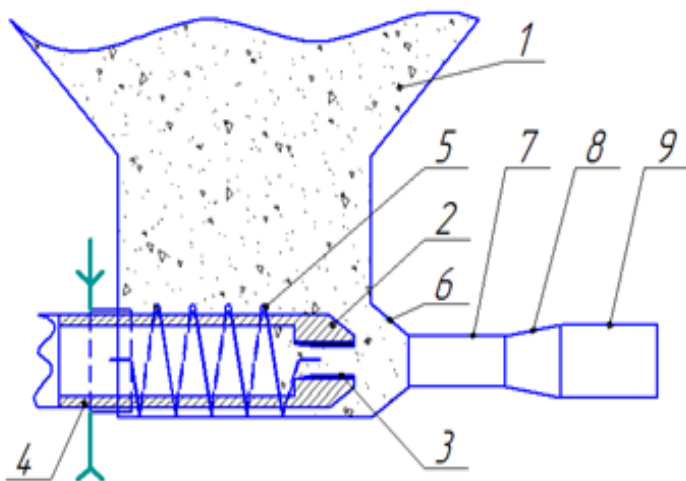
Схема ежекційної установки: 1 - видатковий бункер піноскла; 2 - порожнистий шнековий дозатор-живильник; 3 - робоче сопло шнекового дозатора-живильника; 4 - привідний частина шнекового дозатора-живильника; 5 - воронітель-живильник пружинного типу; 6 - конфузор; 7 - камера змішування (розгінна трубка); 8 - дифузор; 9 - фланець.
